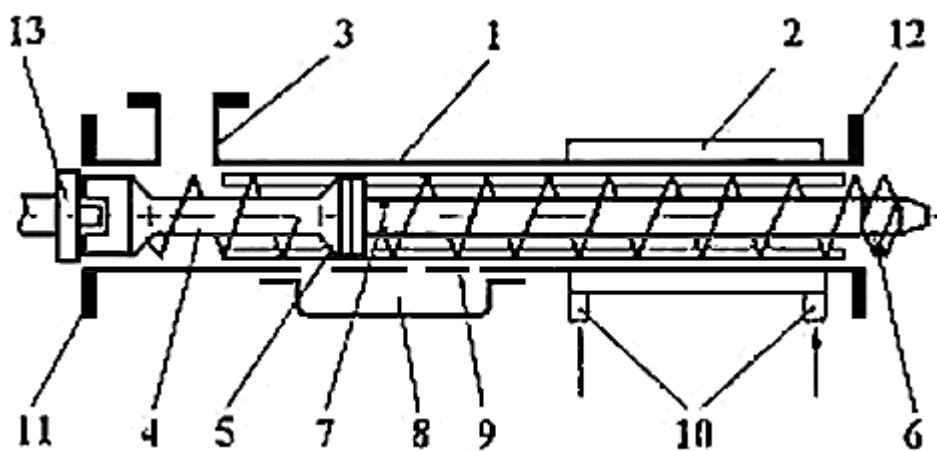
Схема пресувального шнека преса з вакуумуванням тіста у процесі пресування: 1 - циліндр; 2 - охолоджуюча сорочка; 3 - живильний патрубок; 4 - пресувальний шнек; 5 - роз'єднувальна шайба; 6 - тризахідна ланка шнека; 7 - отвір для приєднання вакуум-клапана; 8 - перепускний канал; 9 - розподільча решітка; 10 - штуцери для підведення і відведення охолоджуючої води; 11,12 - приєднувальні фланці; 13 - вал редуктора преса;
